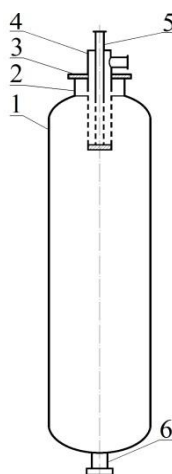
Новый автоклав с обогревом «острым» паром: 1 – корпус; 2 – горловина; 3 – крышка горловины; 4 – патрубок ввода пульпы; 5 – патрубок ввода пара; 6 – патрубок слива пульпы
